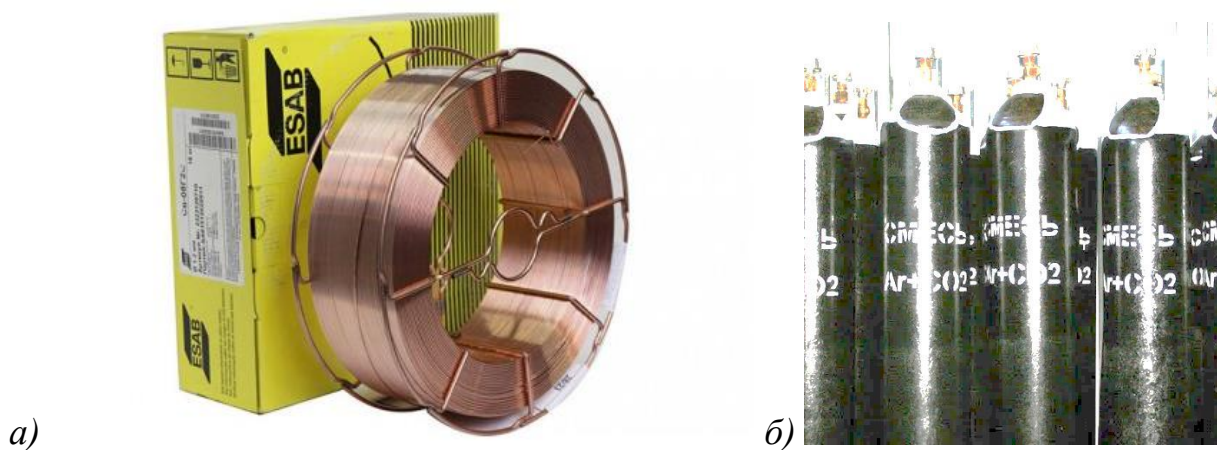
Применяемые сварочные материалы: сварочная проволока Св-08Г2С (а) и смесь газов «аргон + углекислый газ» (б)
